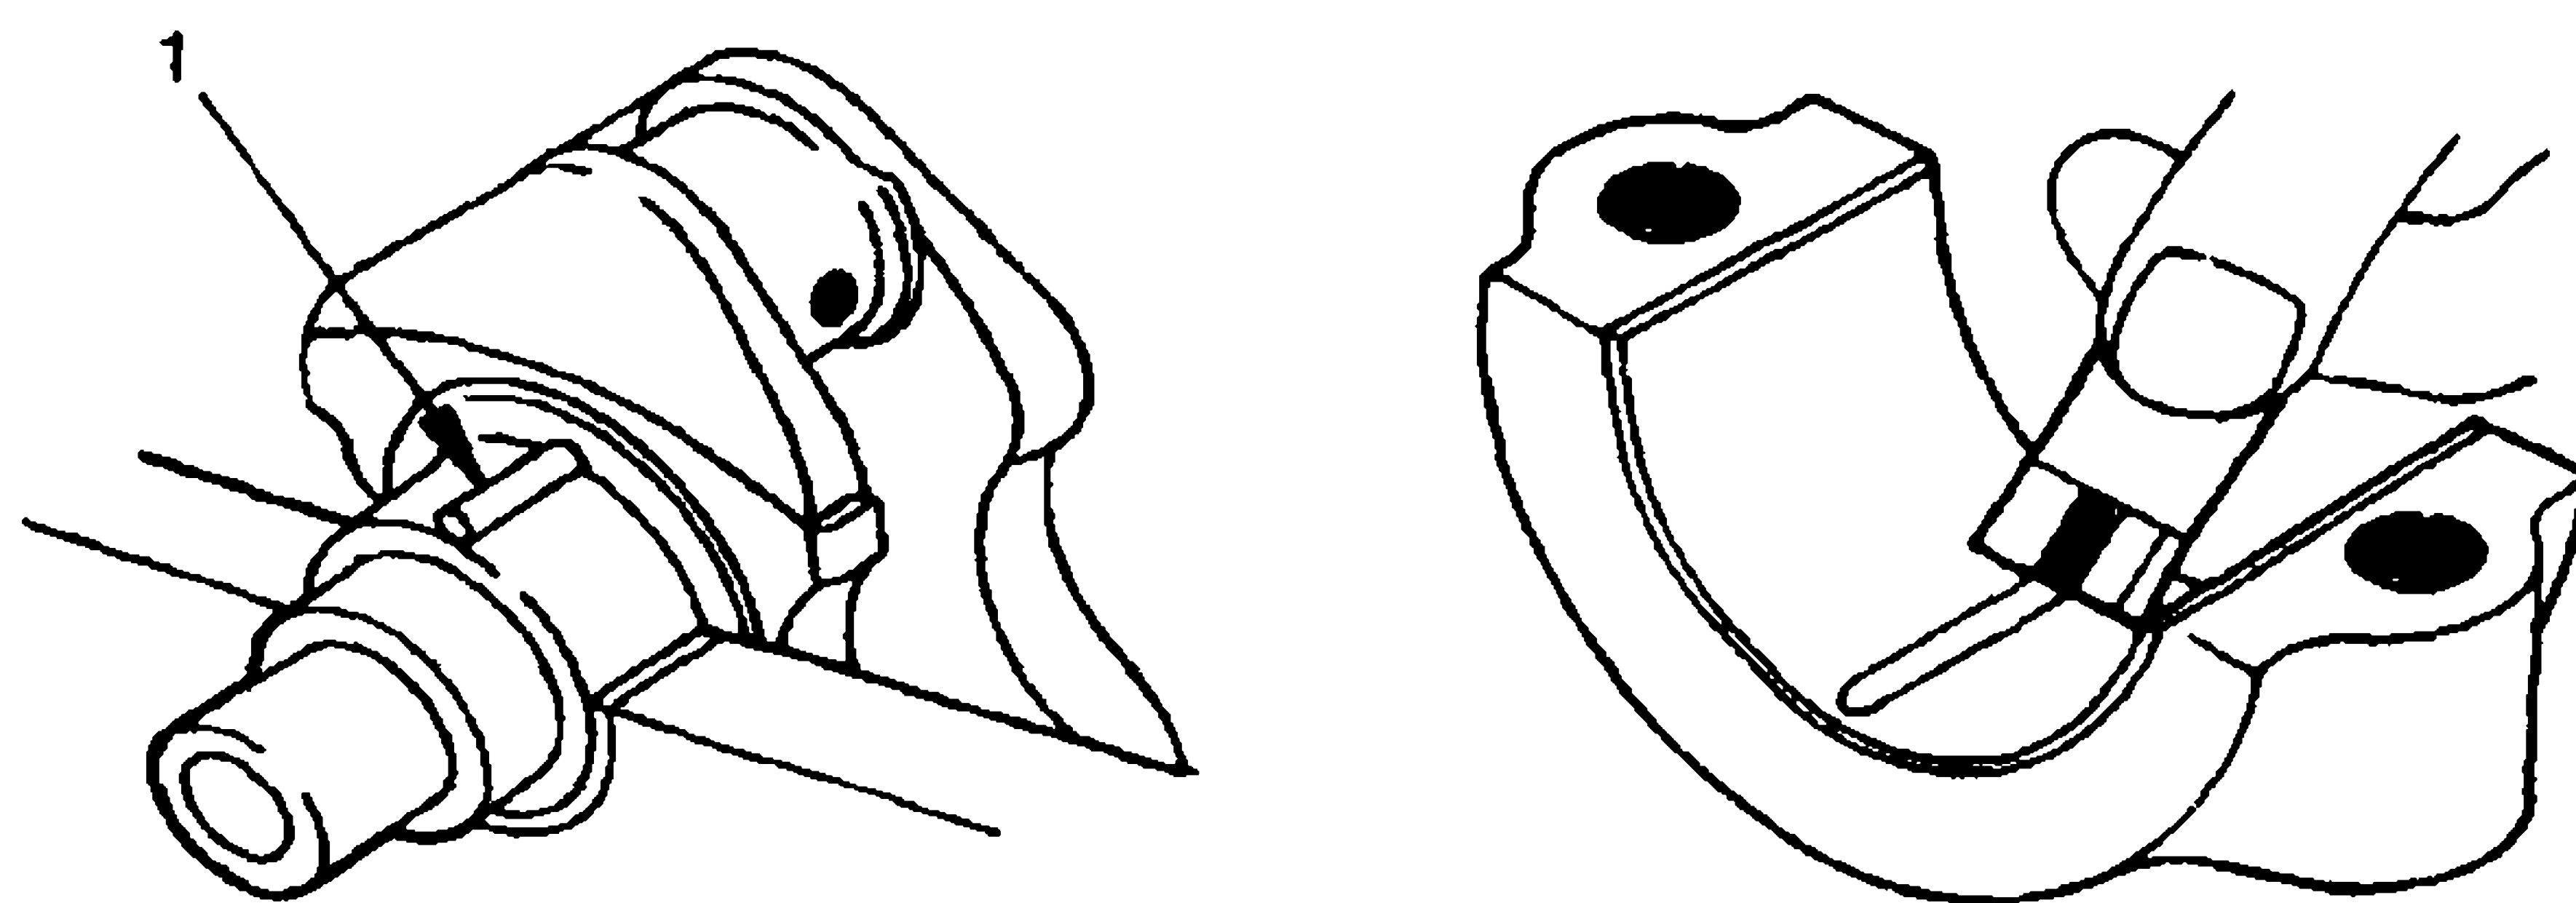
Использование деформации мягкой проволоки (1) для измерения зазоров в подшипниках распредвала и коленвала
